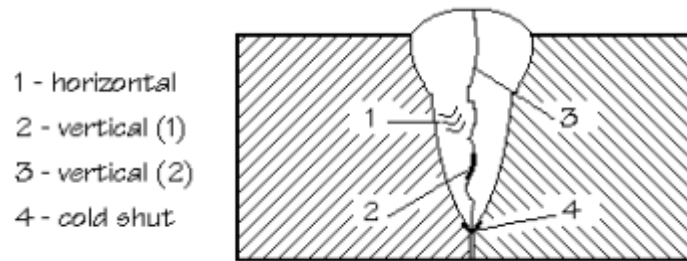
Trincas na soldagem por feixe de elétrons
